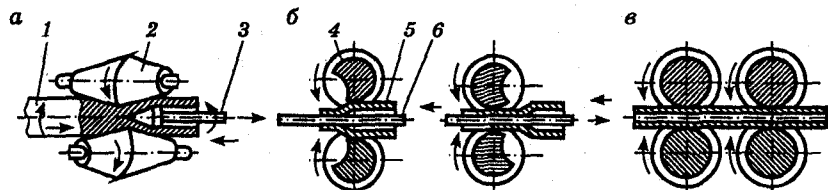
Схема прокатки бесшовных труб на трубопрокатной установке с пилигримовым станом:
